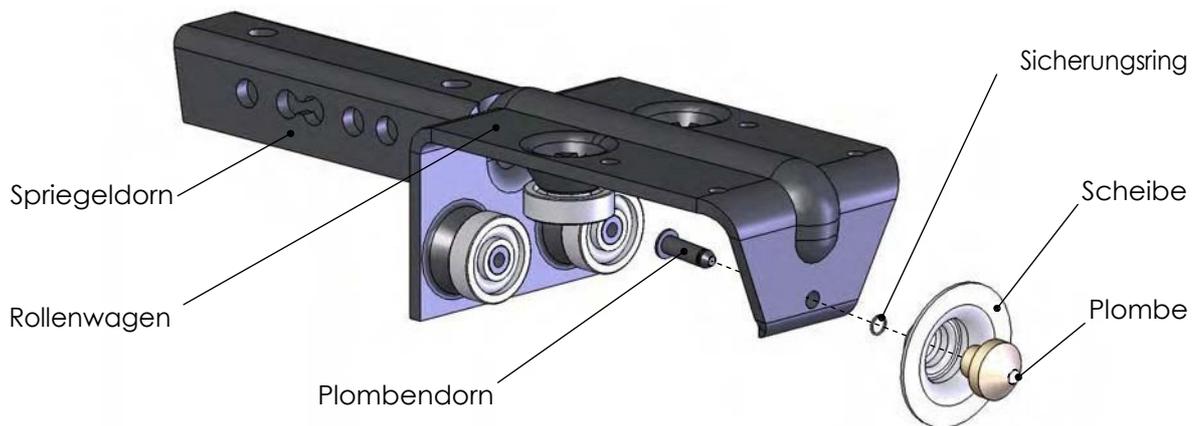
Detailansicht Rollenwagen und Plombe
